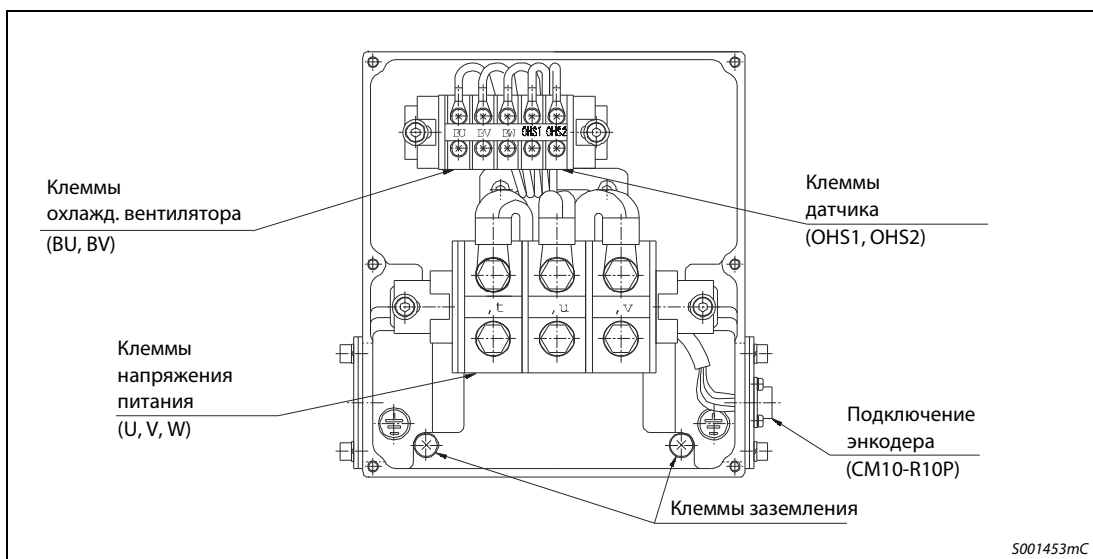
Клеммная коробка двигателей HA-LP15K2(4)(B) и HA-LP22K2(4)(B)
